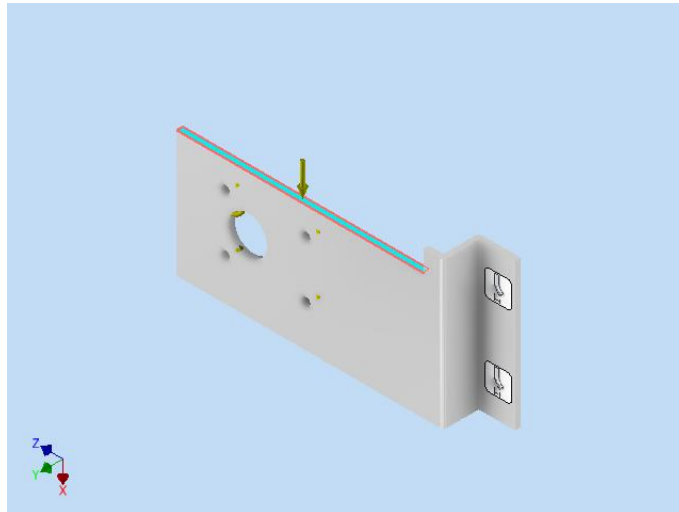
Cara(s) seleccionada(s) – Fuerza - Base Motorreductor.
